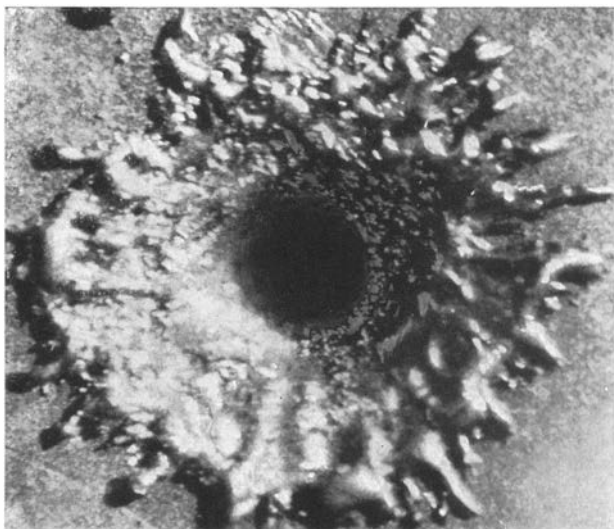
Mit einem Impulslaser erzeugte Bohrlöcher (Seitenansicht)
